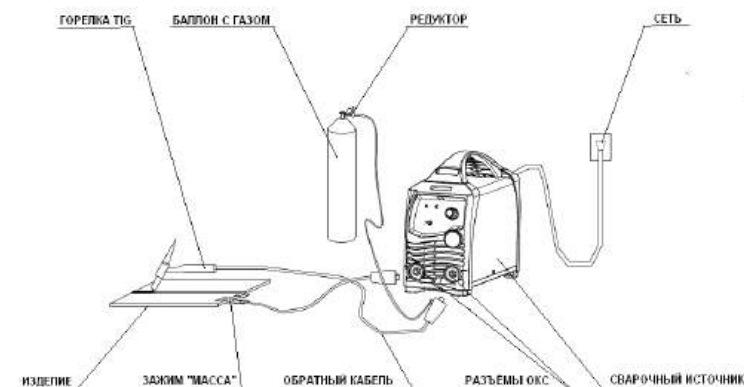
Схем подключения оборудования для TIG сварки
